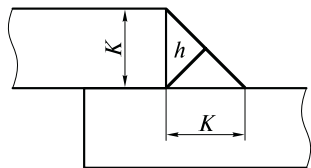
Плоскость разрушения h в сечении углового сварного шва:
